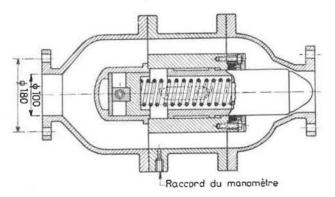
is. — Régulateur d'air automatique « Brieden » pour remblayeuse pneumatique.
